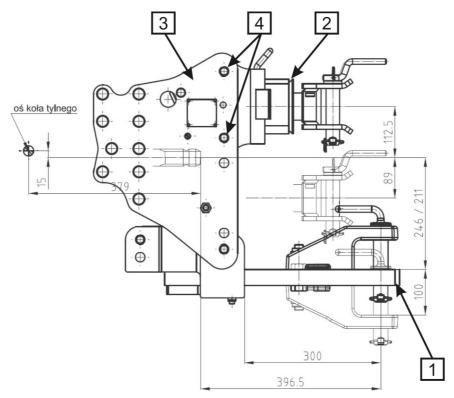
Сцепные устройства тракторов ZEFIR 40 / 40K — устройство и габариты. 1 - сельскохозяйственная сцепка; 2 - буксирное устройство; 3 - монтажный корпус сельскохозяйственной сцепки и буксирного устройства; 4 - крепежные шкворни.
